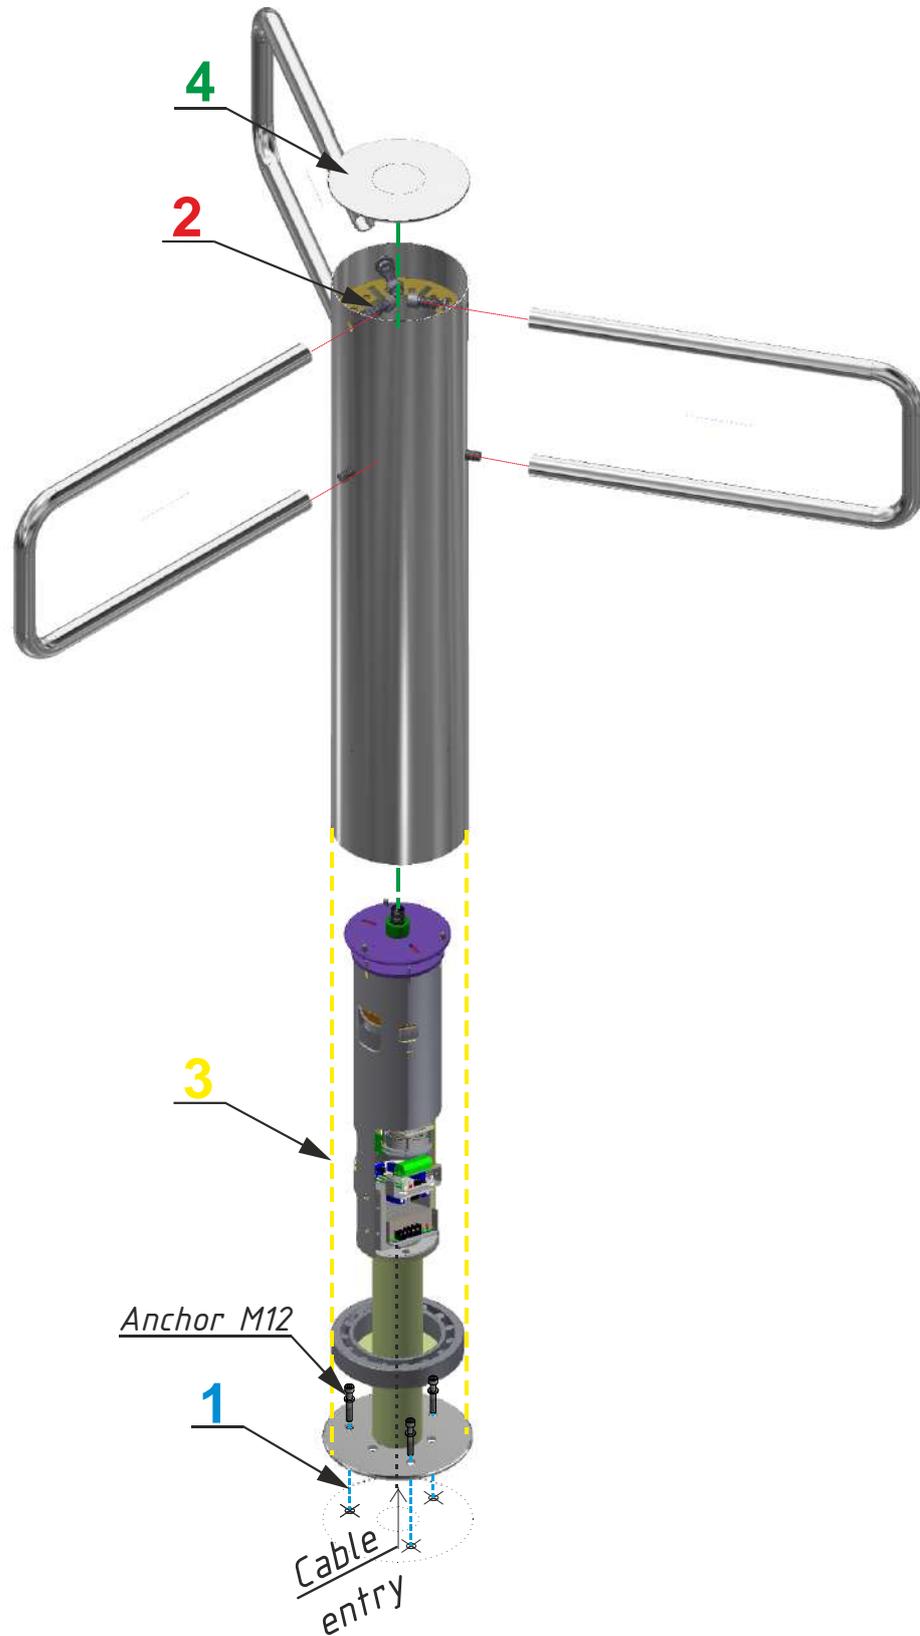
Монтаж и установка турникета роторного с лопастями из нержавеющей стали
